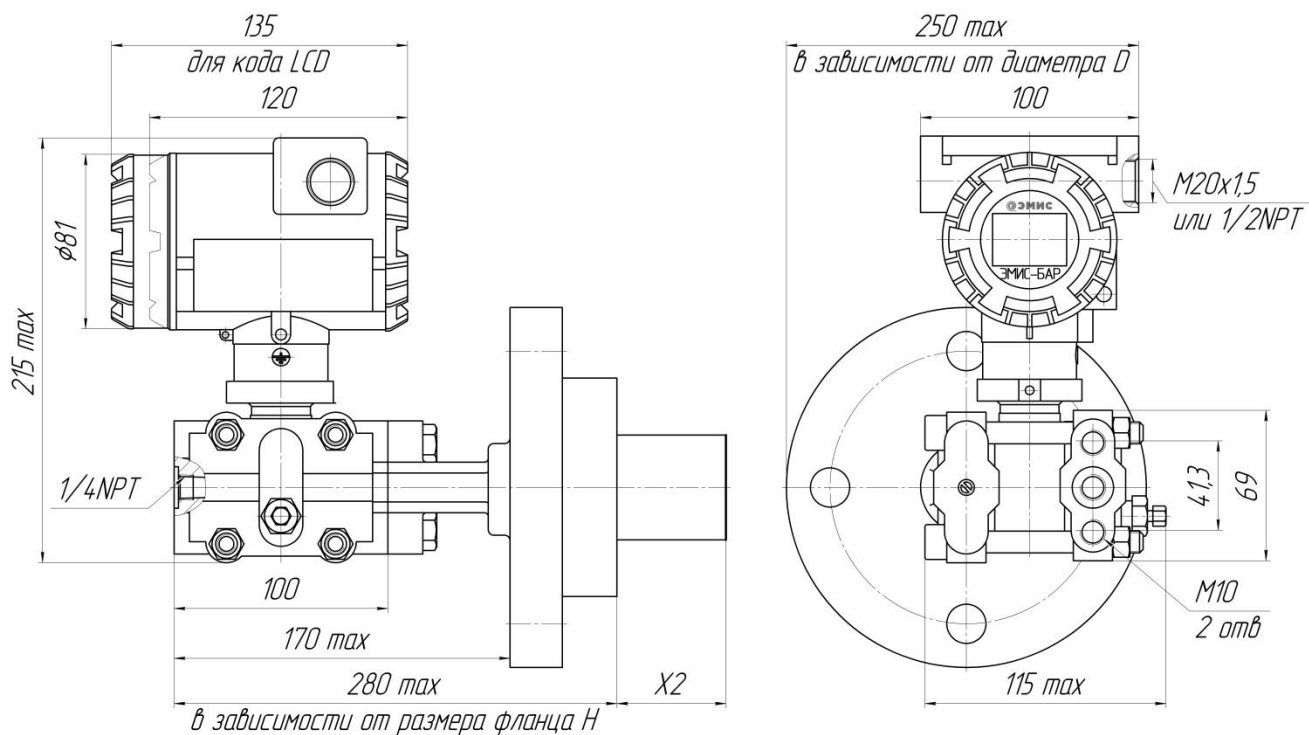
Габаритные и присоединительные размеры штуцерного исполнения с открытой мембраной датчиков давления ЭМИС-БАР 113
